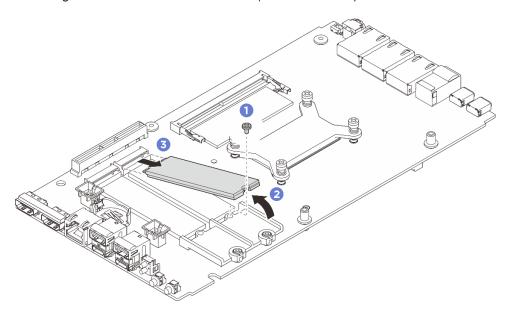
Entfernen des M.2-Laufwerks (Formfaktor 2280)
